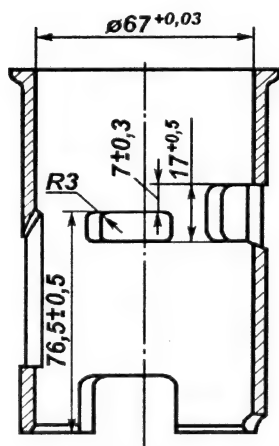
Гильза цилиндра двигателя мотора «Вихрь-М»
